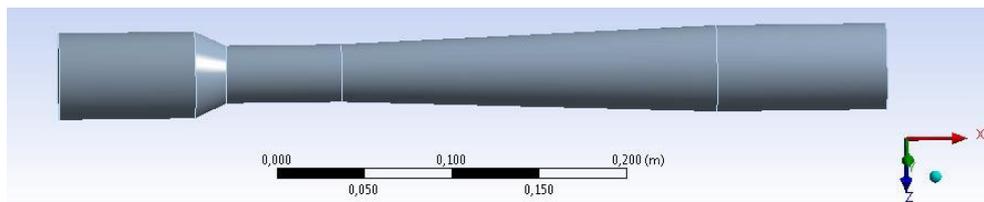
Venturi 4 - Comprimento da garganta 66 mm e Diâmetro da garganta 33 mm.
